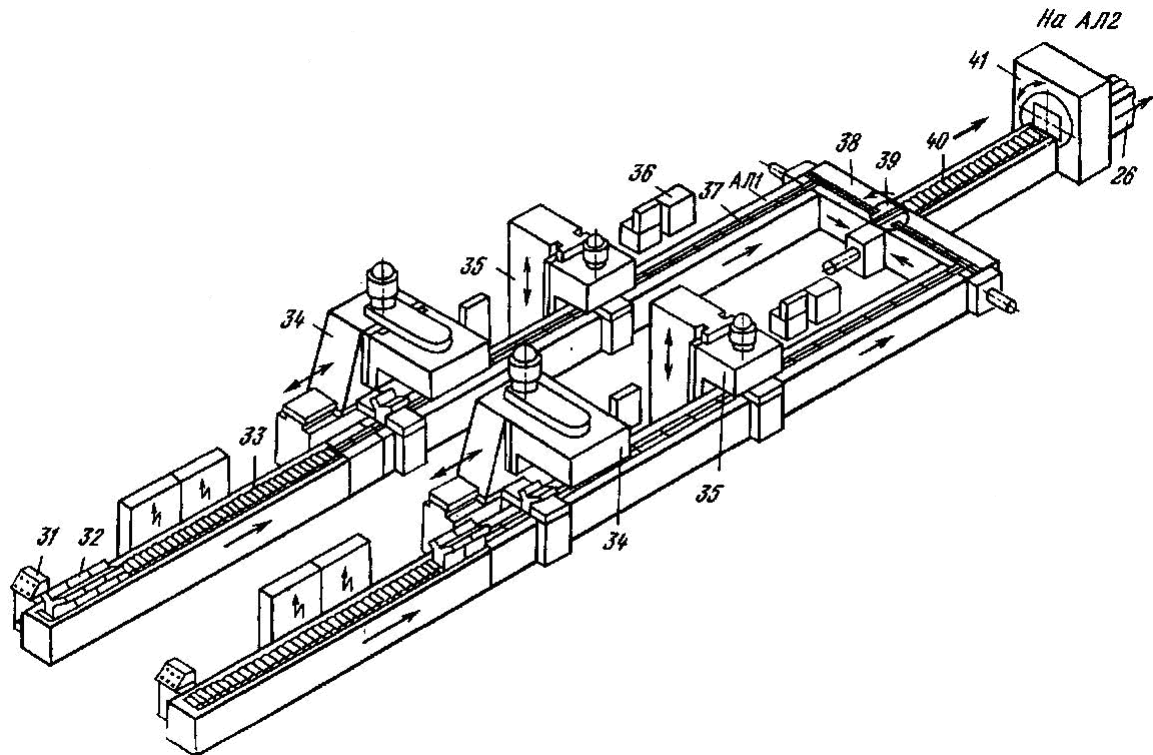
Автоматична лінія для обробки базових поверхонь
